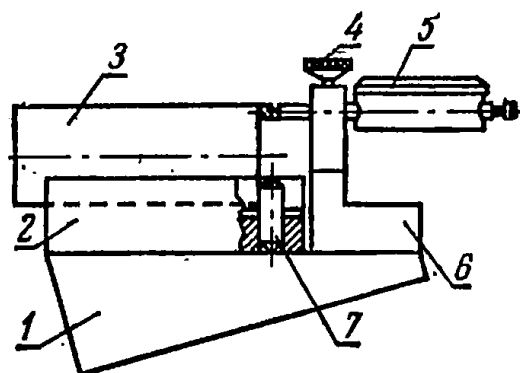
Приспособление для контроля биения торца поршневых пальцев:
